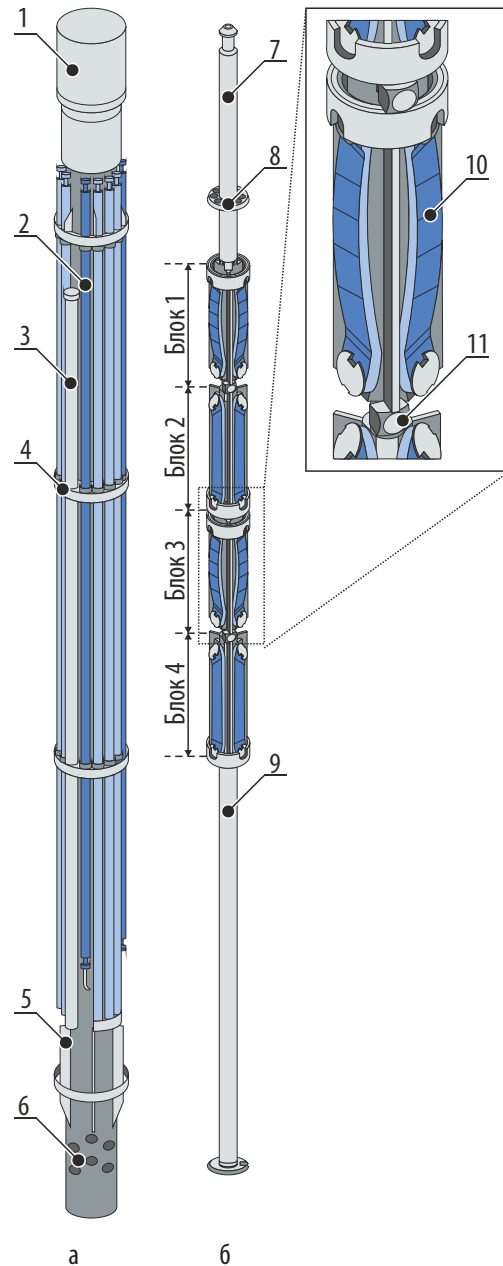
Конструктивная схема элементов облучательного устройства — твэльной сборки (а) и подвески с образцами (б): 1 — разделитель потока; 2 — твэлы; 3 — переливная трубка; 4 — дистанционирующая решётка; 5 — рёбра; 6 — хвостовик ТВС; 7 — головка подвески; 8 — опорная решётка; 9 — хвостовик подвески; 10 — образцы конструкционных материалов; 11 — штифт
